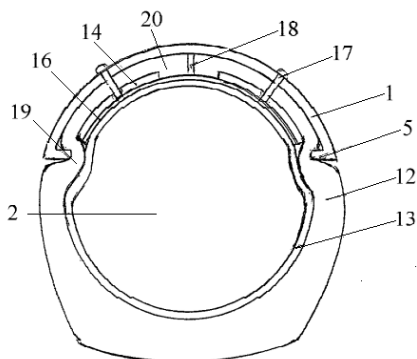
Пневматична шина: 1 – секція обода; 2 – шина; 5 – відсортуння; 12 – покриття; 13 – камера; 14 – пластина; 16 – прокладка; 17 – гвинти; 18 – поздовжній розріз; 19 – вигини
